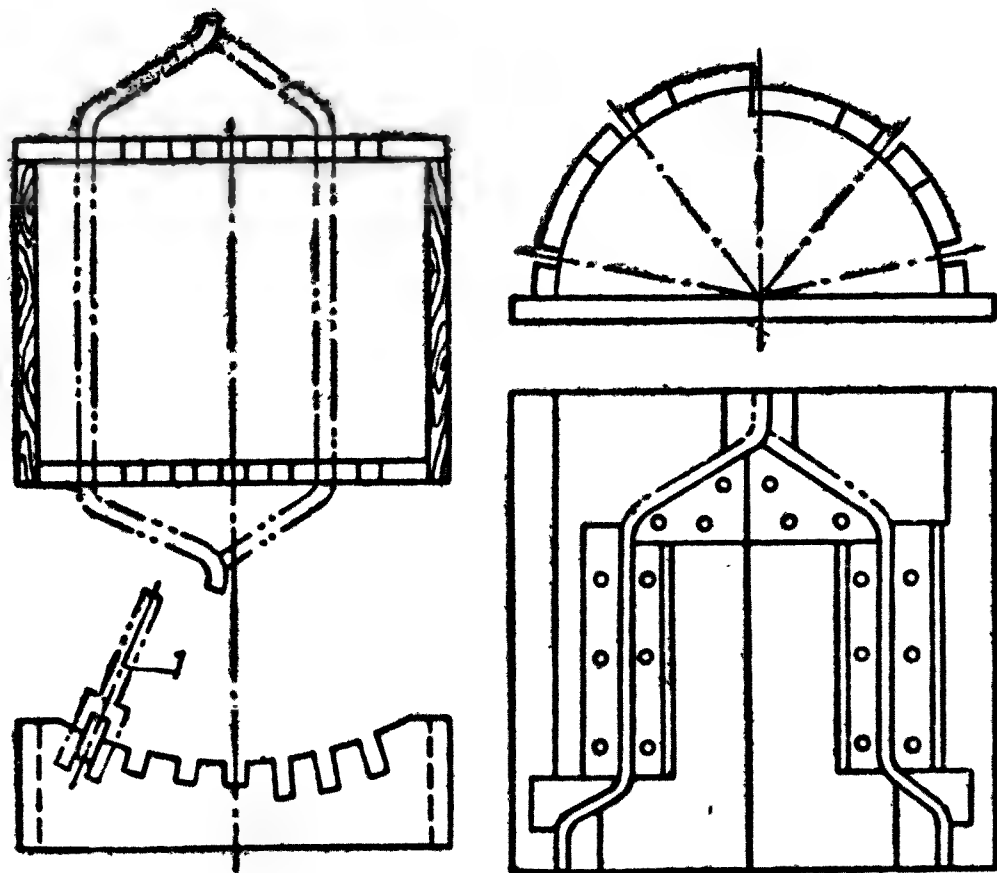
Макет для формовки секций (1 — вилка для рихтовки).
